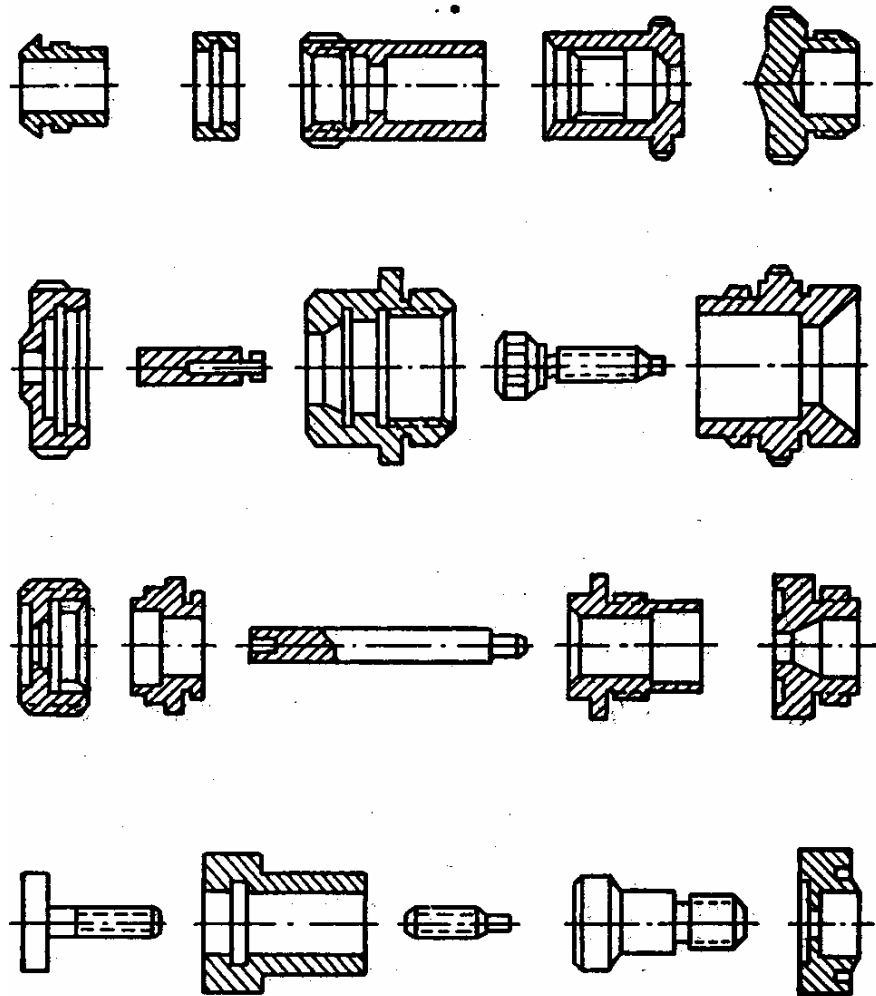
Детали, обрабатываемые на револьверных станках.
